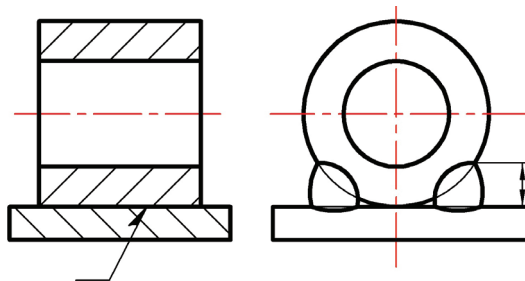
Условное изображение и обозначение нестандартного шва сварного соединения
